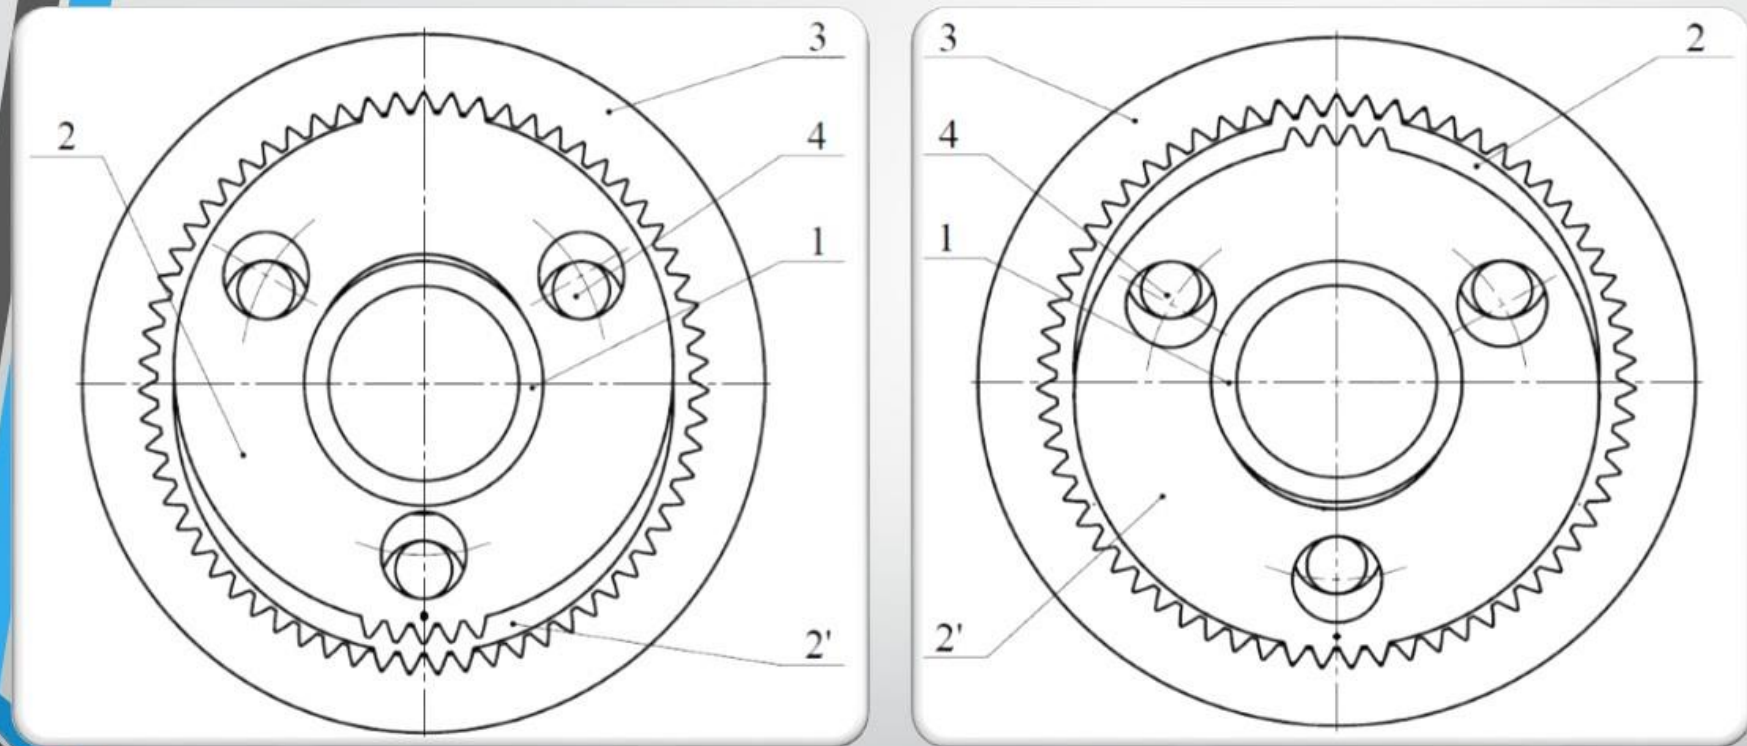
Вигляд кривошипно-планетарного редуктора зі сторони сателітів
